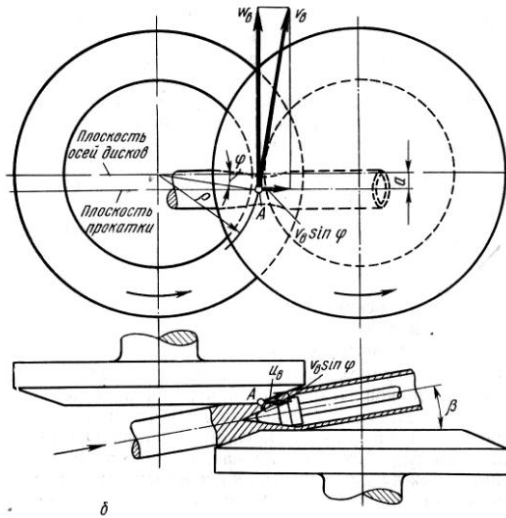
Схема поперечно-гвинтової прокатки у валках зі зміщеною віссю заготовки
